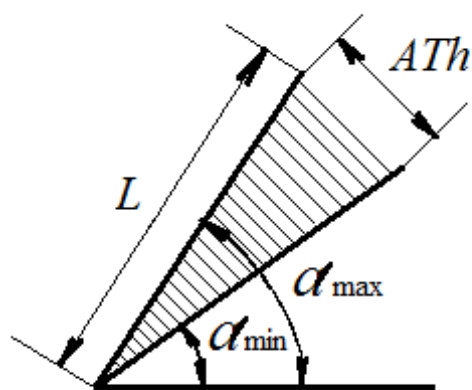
Способы выражения допуска на угловые размеры
